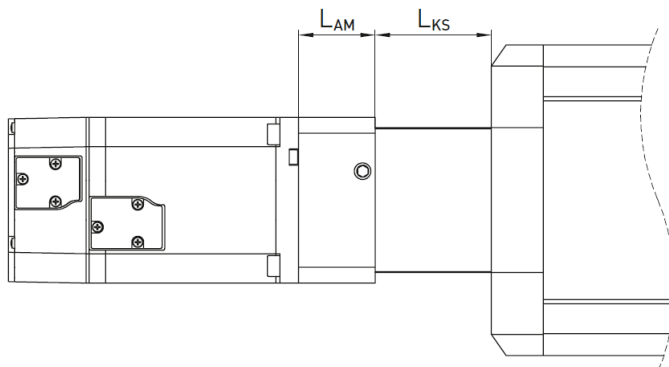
Motoranbindung Linearmodule HM-S ohne Riementrieb
